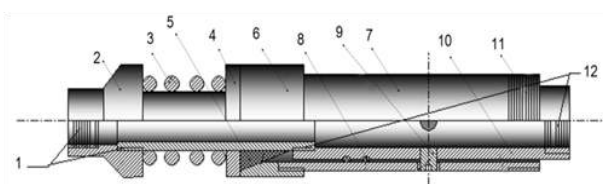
Отцепное устройство со срезными штифтами: 1 - резьба трубная 73 мм; 2 - ограничитель-переводник; 3 - демпфер (пружина); 4 - кольцо упорное; 5 - сальниковый конус; 6 - воронка направляющая; 7 - корпус спецпереводника диаметром 114 мм; 8 - сальниковое уплотнение; 9 - срезной штифт; 10 - ствол спецпереводника; 11 - резьба трубная 114 мм; 12 - резьба трубная 73 мм
